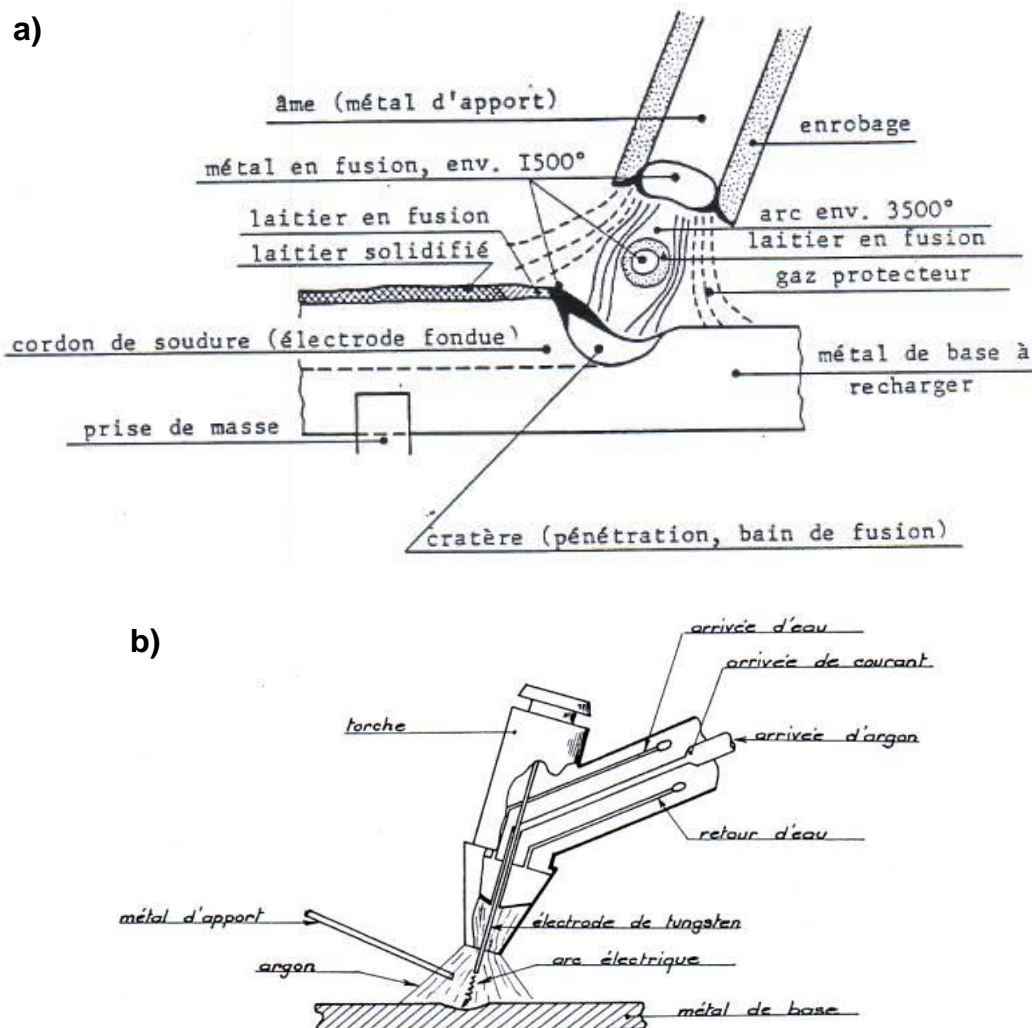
Schémas de principe des techniques de soudage à l'arc (a) à l'électrode enrobée et (b) Tungsten Inert Gas [92]
